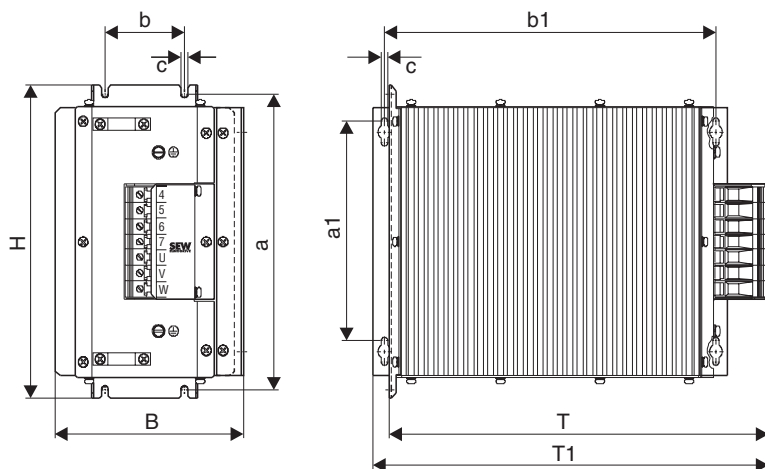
Габаритный чертеж выходного фильтра HF450-503
